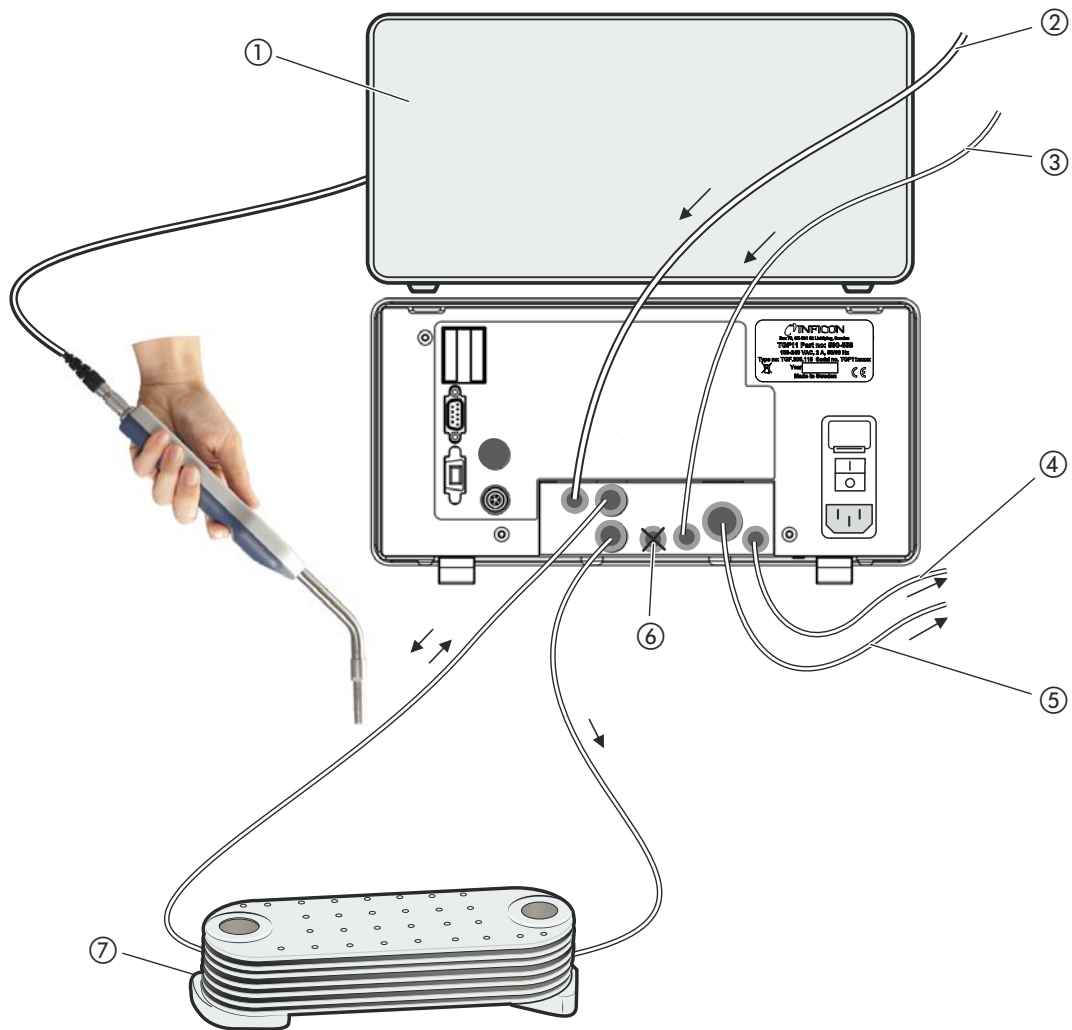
Prüfaufbau zur Gasbefüllung des Prüfobjekts mit Prüfgas über die Prüfanschlüsse 1 und 2
